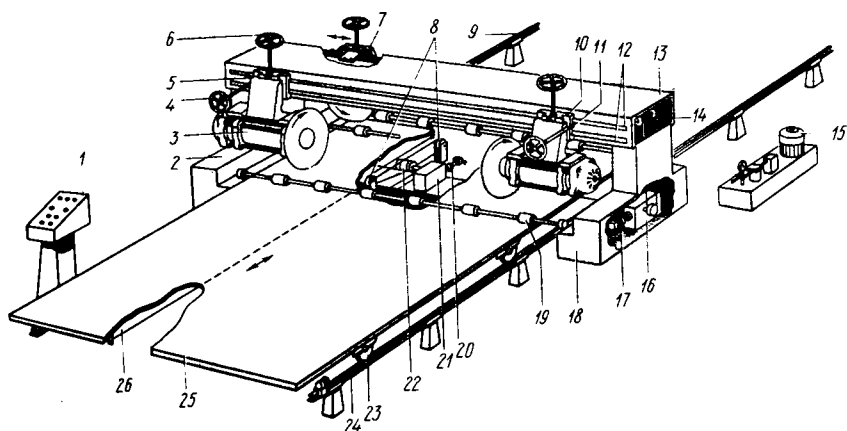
Кинематическая схема трехпильного форматного станка ЦТЗФ-1:
